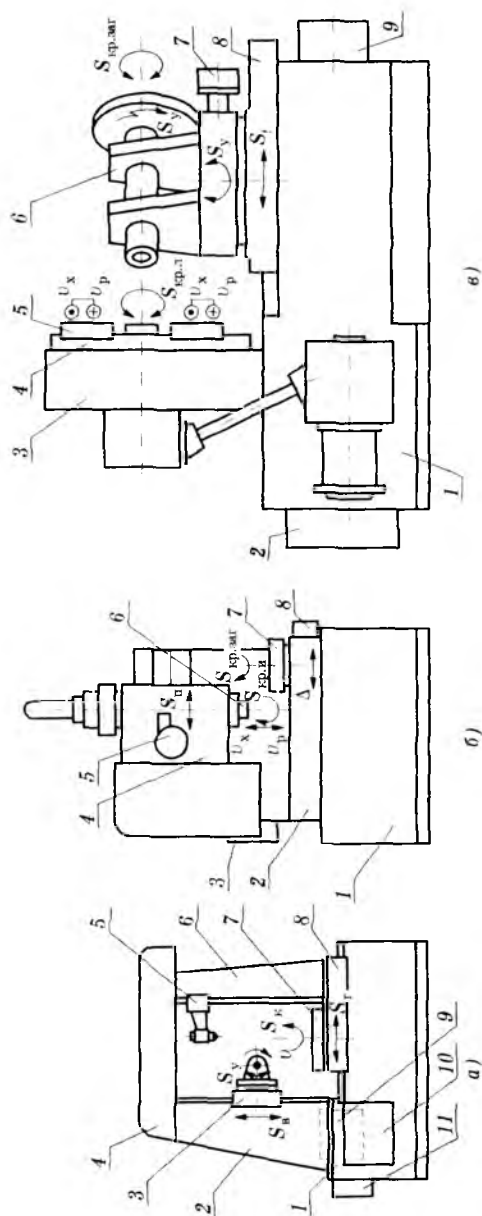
Схемы конструкций зубопрофилирующих станков:
